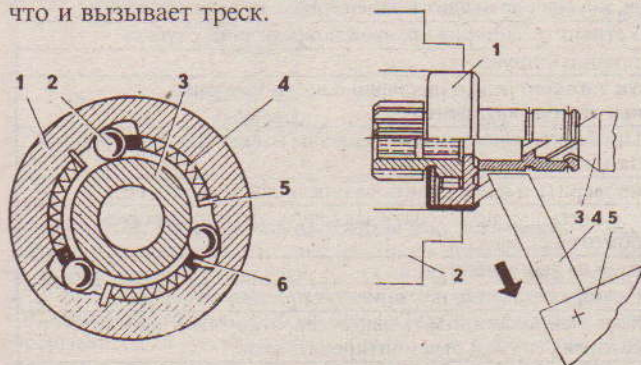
Муфта свободного хода привода стартера: 1 - наружная ведущая обойма; 2 - ролик; 3 - внутренняя ведомая обойма (шестерня); 4 - пружина; 5 - лепесток пластины (упор пружины); 6 - толкатель
